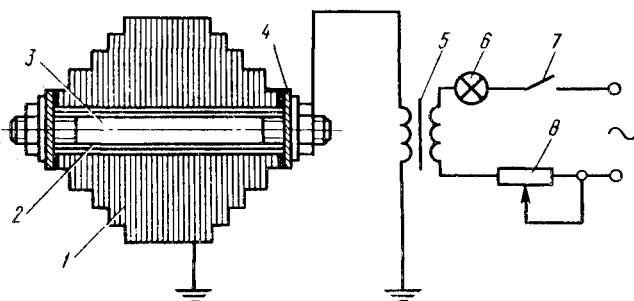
Схема испытания изоляции стяжных шпилек магнитопровода:
